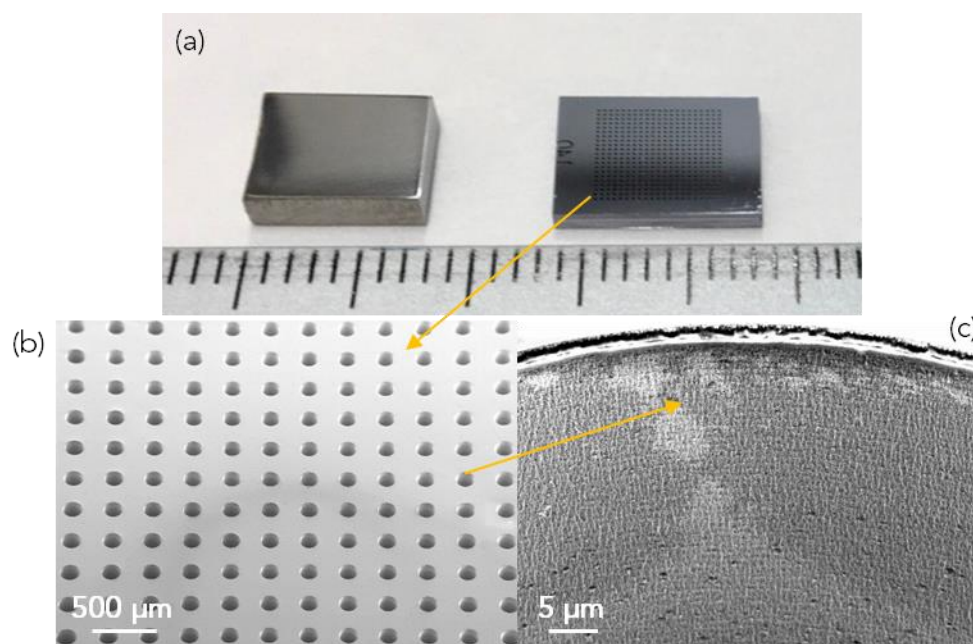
1 : Photographie d'une plaque de verre métallique ZrCoAl à thermoformer (a) sur le moule en Si comportant des cavités cylindriques de 140 µm de diamètre et images en MEB des cavités du moules à deux grossissements (b) et (c)
